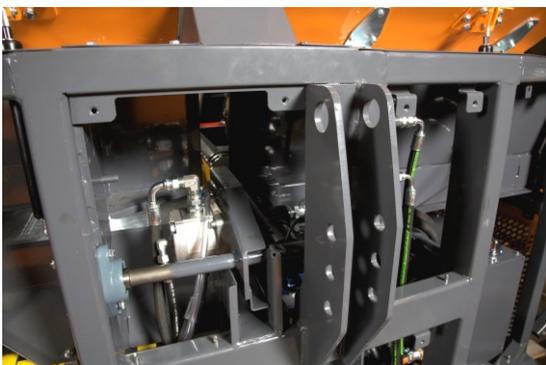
Paliers de bride du mécanisme de fendage 2 graisseurs
